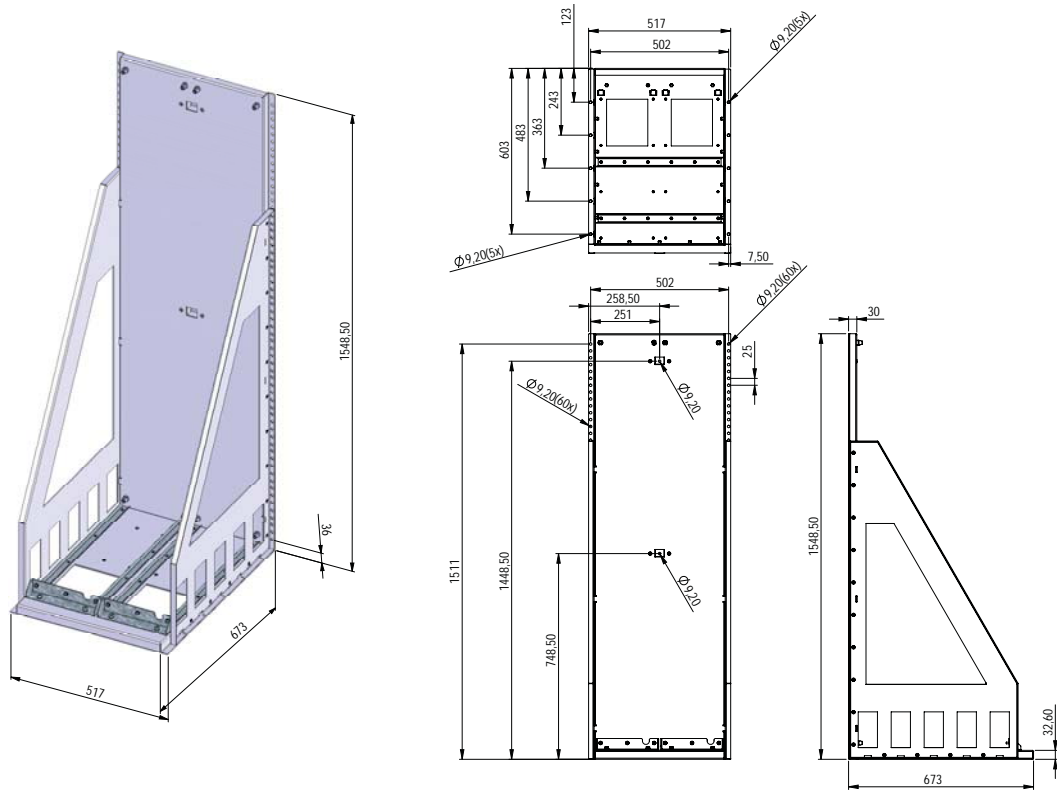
Rack para Modular Drive (1 ou 2 books)
